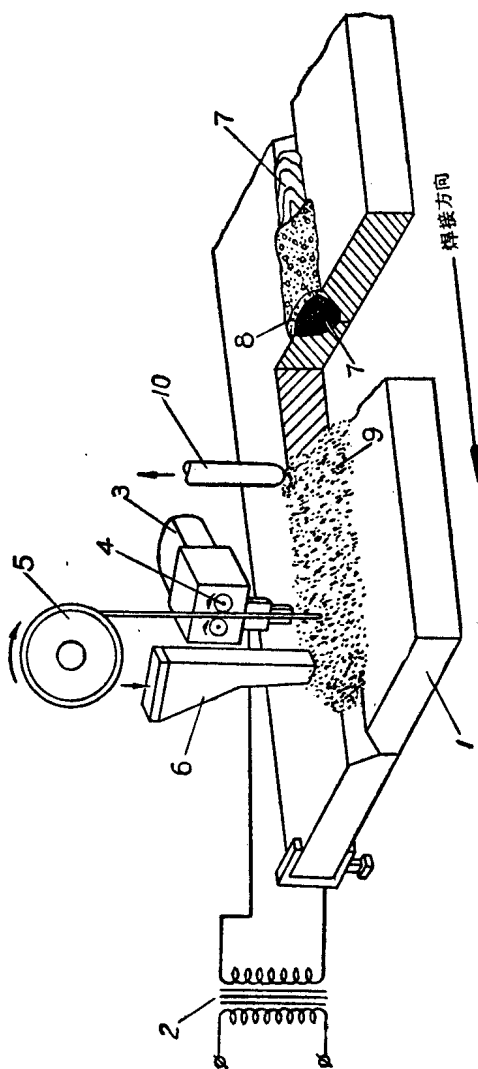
焊剂層下自动电弧焊的焊接过程:
